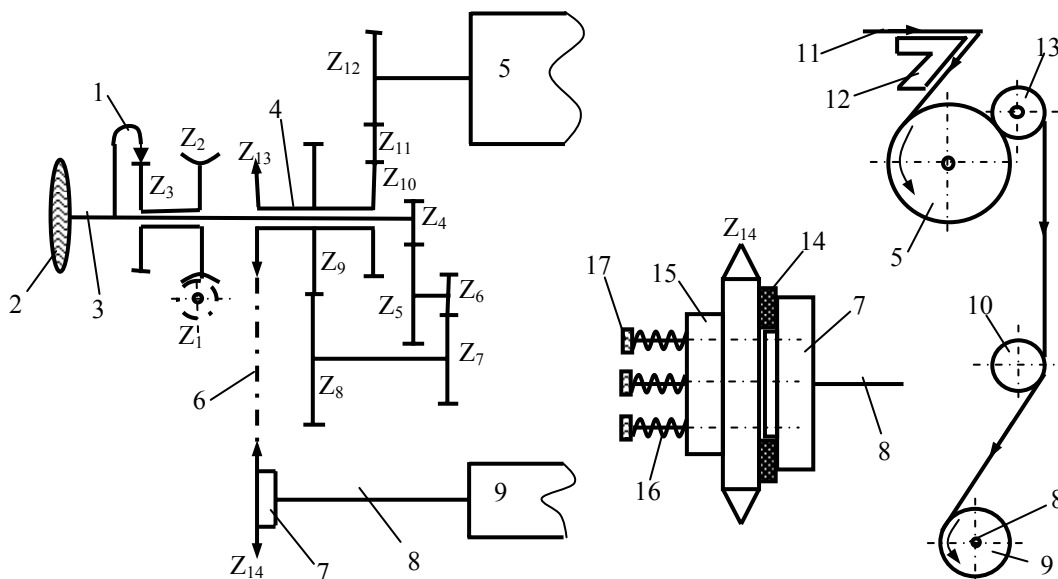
Regulatorul pozitiv pe mașina de țesut cu proiectil
